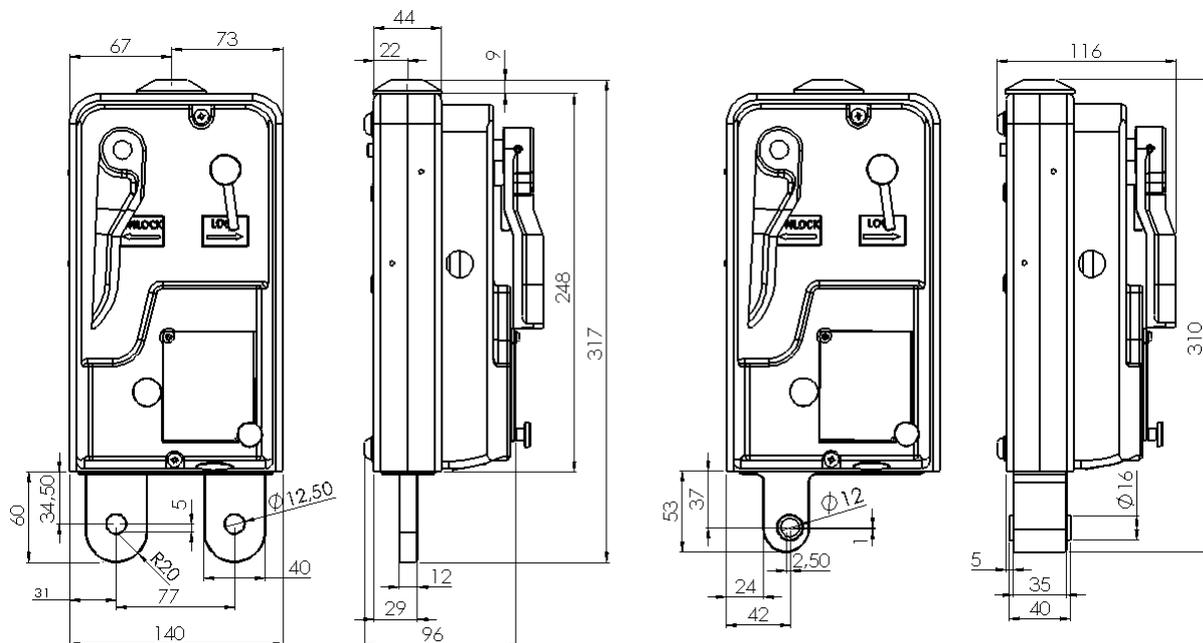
Abmessungen des OSL-T (links: Double Seat, rechts: Single Seat)
